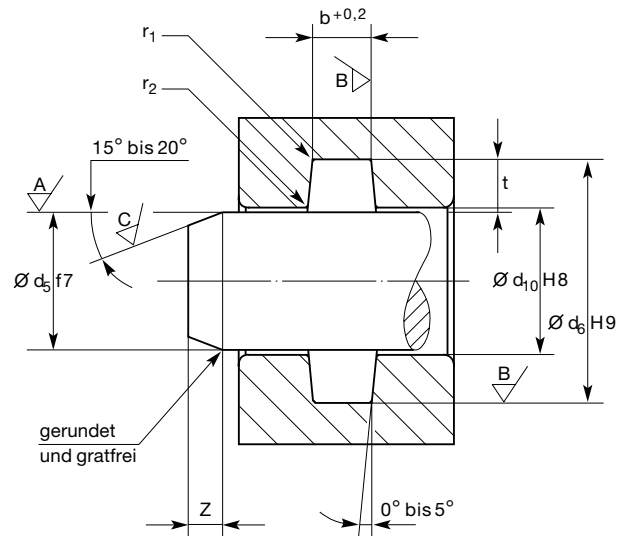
Stangendichtung – Hydraulik und Pneumatik
